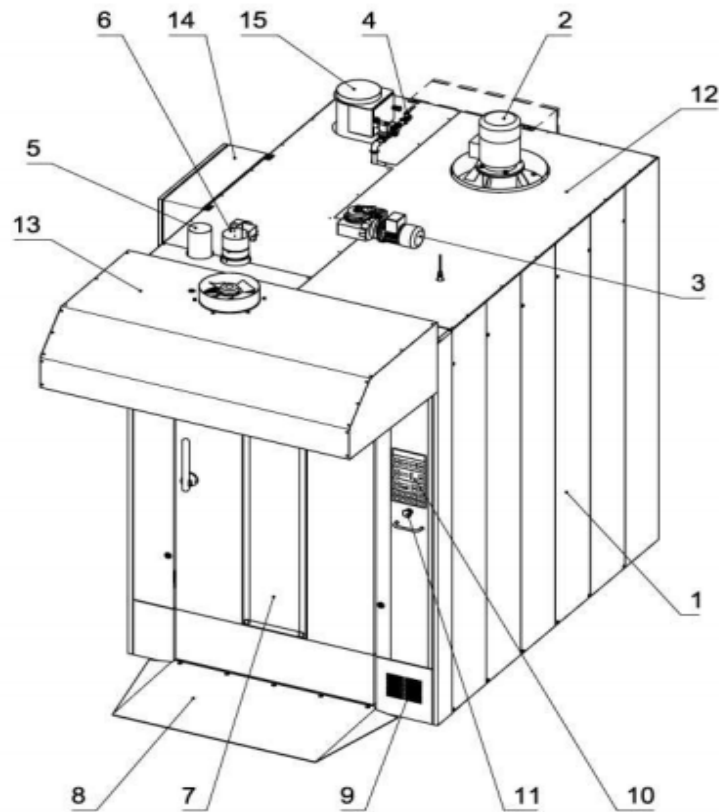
Загальний вигляд та компонування ротаційної печі «Winkler» 1 – корпус; 2 – вакуум-барабан (вентиляторний блок); 3 – привід обертання візка; 4 – лінія парогенератора; 5 – вузол паровидалення; 6 – регульовальна заслінка; 7 – термодвері; 8 – завантажувальний трап; 9 – система охолодження; 10 – панель інтерфейсу; 11 – аварійний стоп-сигнал; 12 – кріплення панелей; 13 – вентиляційний козирок; 14 – електрошафа; 15 – димовідвідний патрубок.
